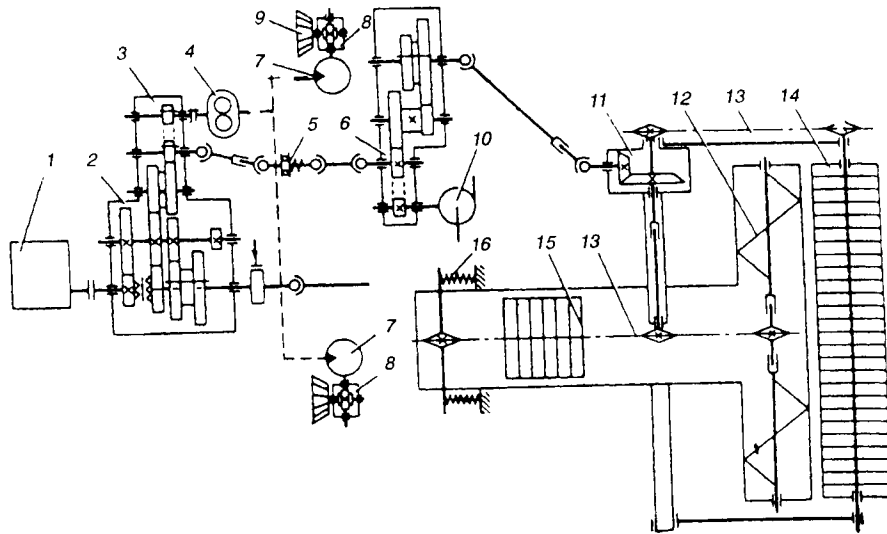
Кинематическая схема подметально-уборочной машины
